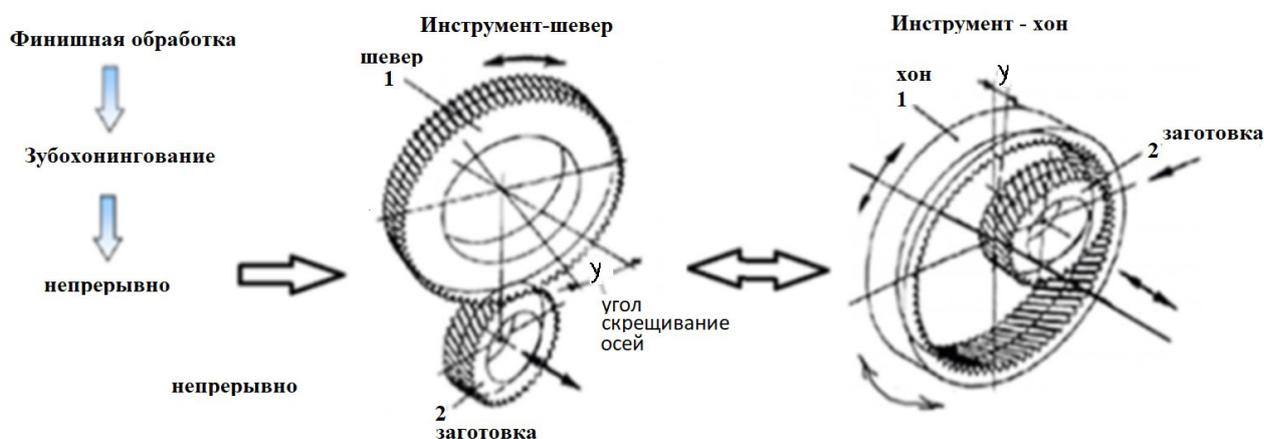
Схема смещения обработки детали с помощью хона или шевера
